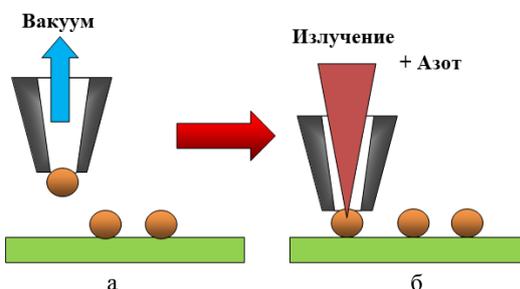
Припойный шарик перед присоединением под торцом сварочного инструмента (а); припойный шарик в позиции присоединения (б)
